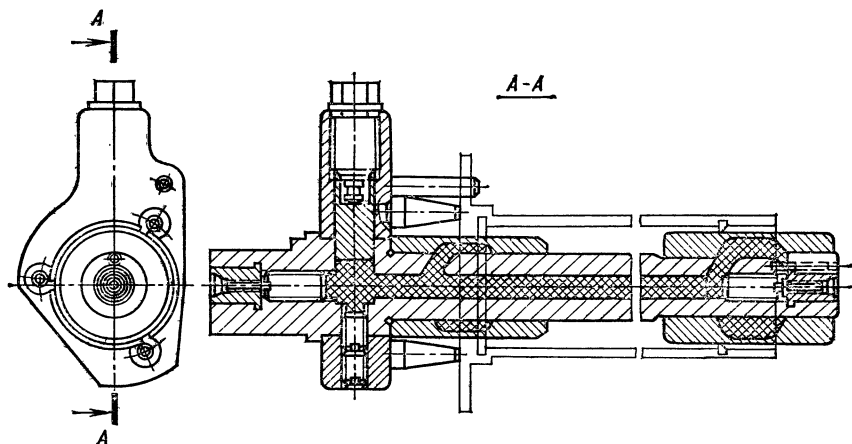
Гидропластмассовое приспособление для точной обработки тонкостенной заготовки
